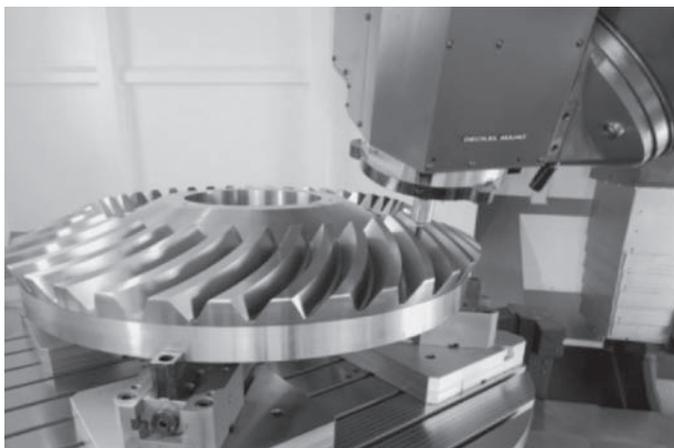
Fresado de un engranaje en una máquina de DMG-MoriSeiki
